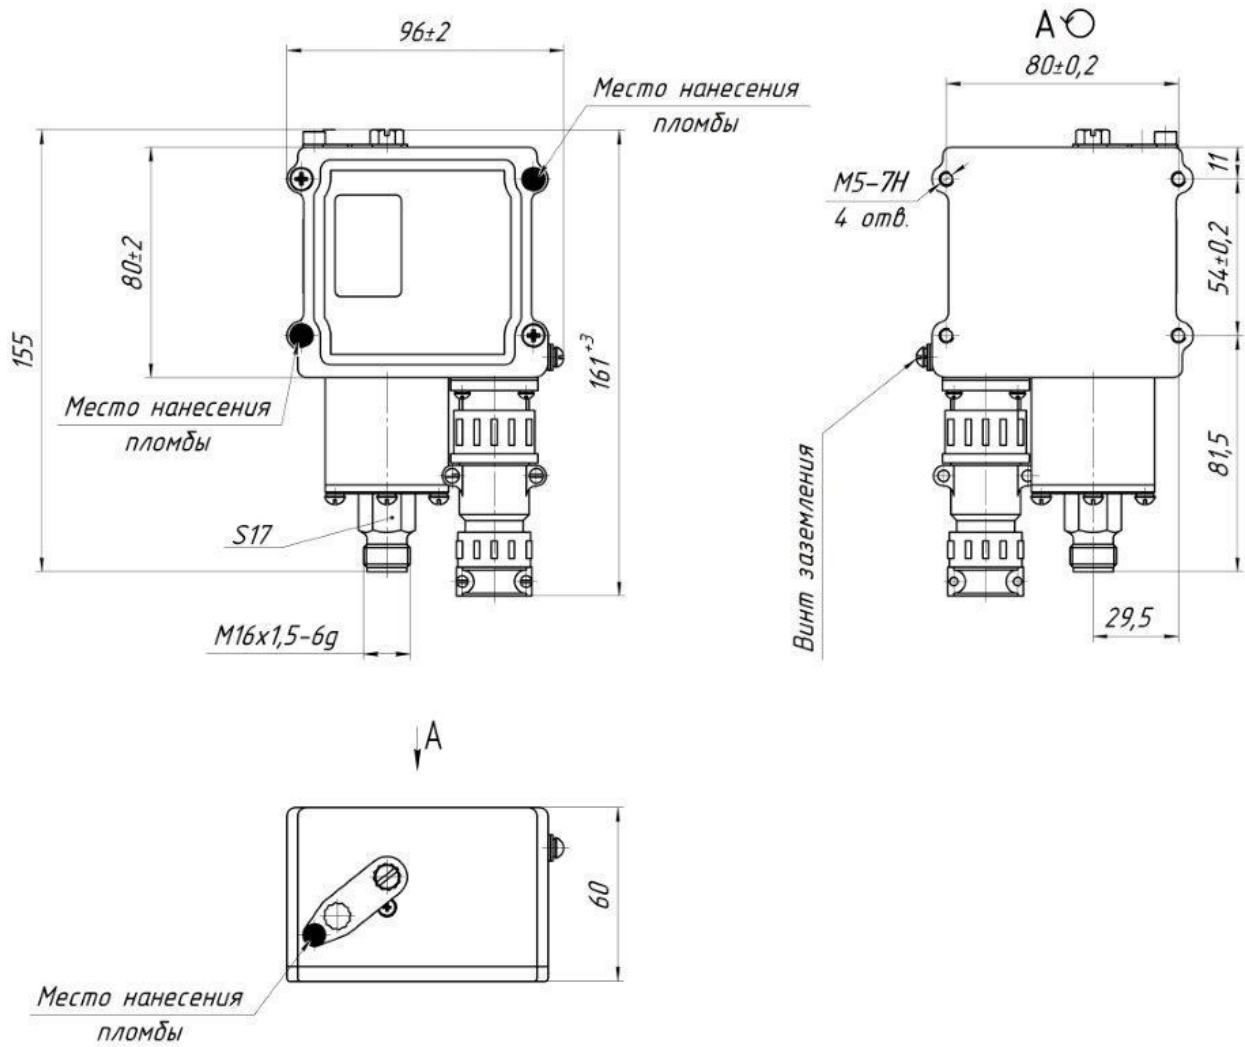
Габаритные и установочные размеры прибора с соединителем типа 2РТТ, ШР с прямым патрубком
